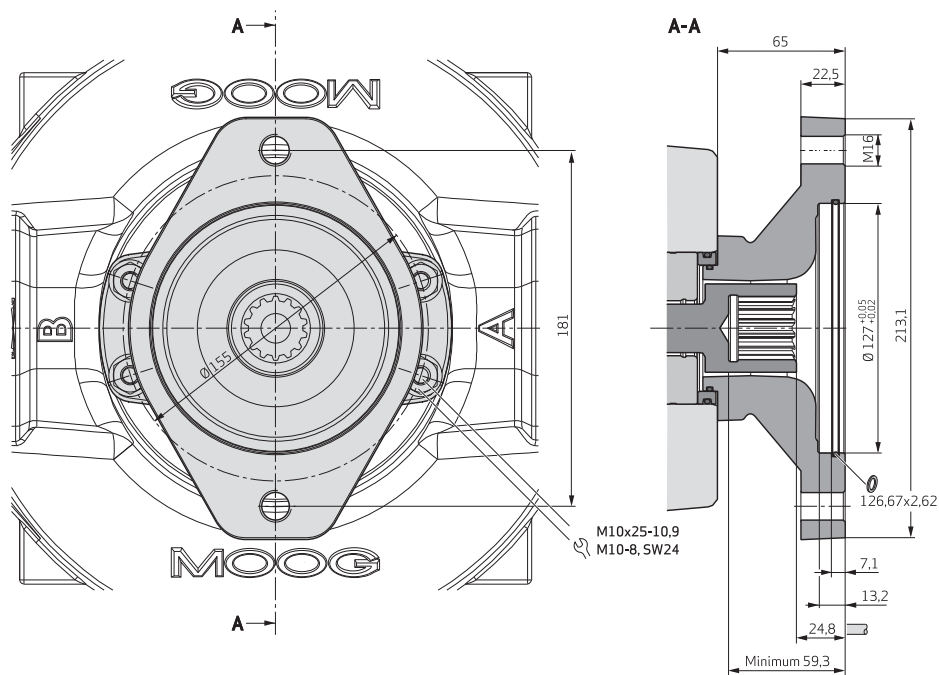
Adapterflansch SAE-C mit 14-zahniger Welle
